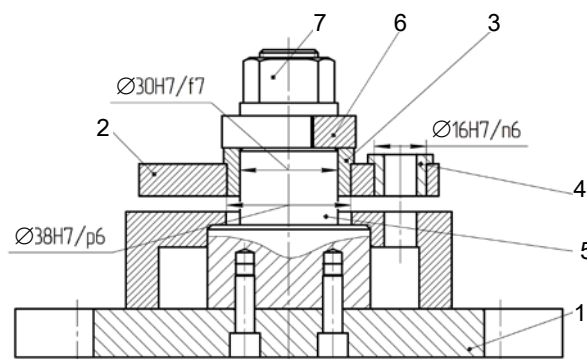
Конструктивная схема кондуктора: 1 – основание; 2 – плита; 3 – втулка; 4 – кондукторная втулка; 5 – ось; 6 – быстросъемная шайба; 7 – гайка
